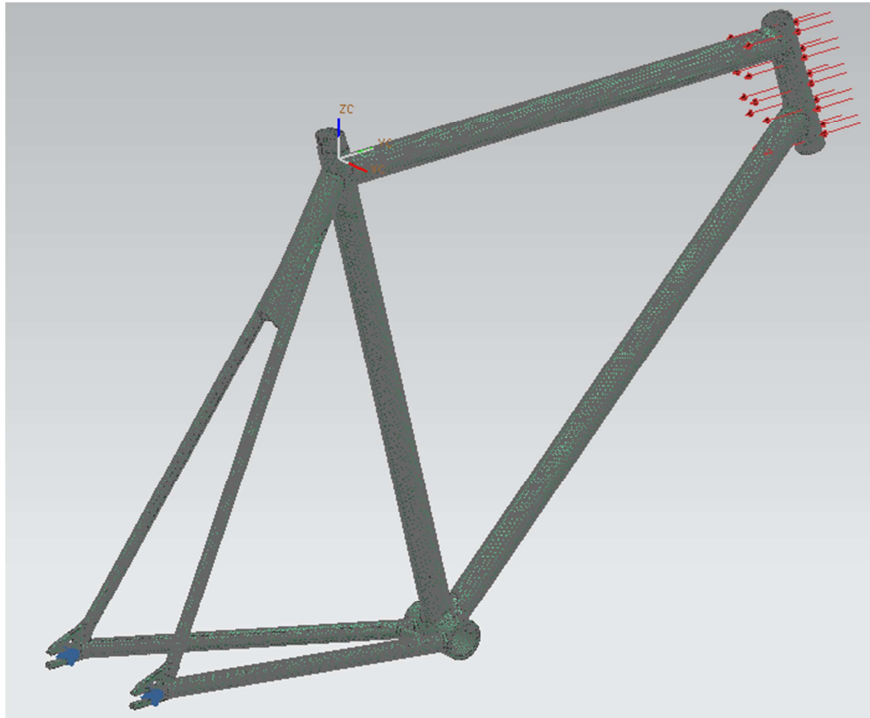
Fuerzas y puntos fijos del ensayo de choque.
